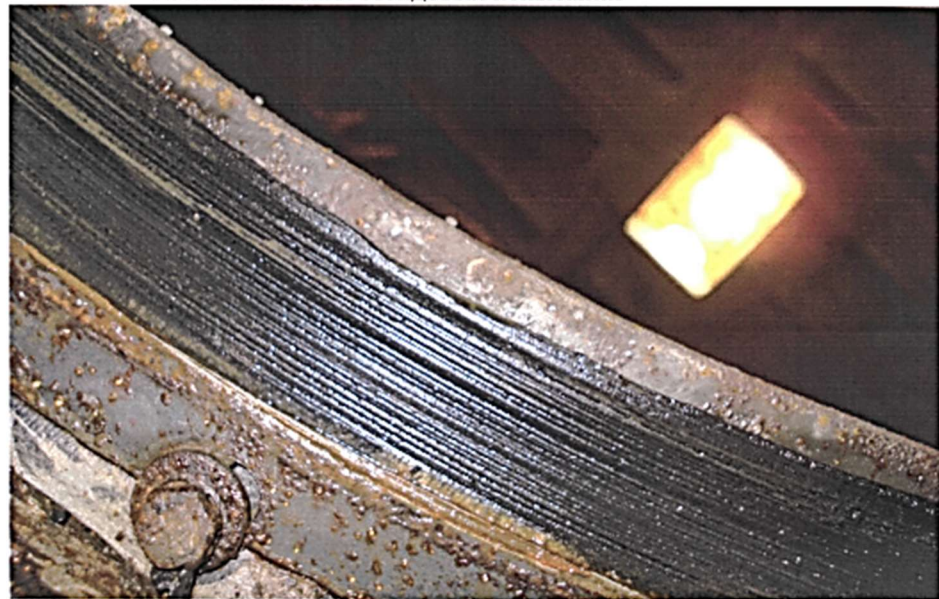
Верхнее неподвижное кольцо гидроуплотнения ЦОМ-5 после окончания стендовых испытаний
